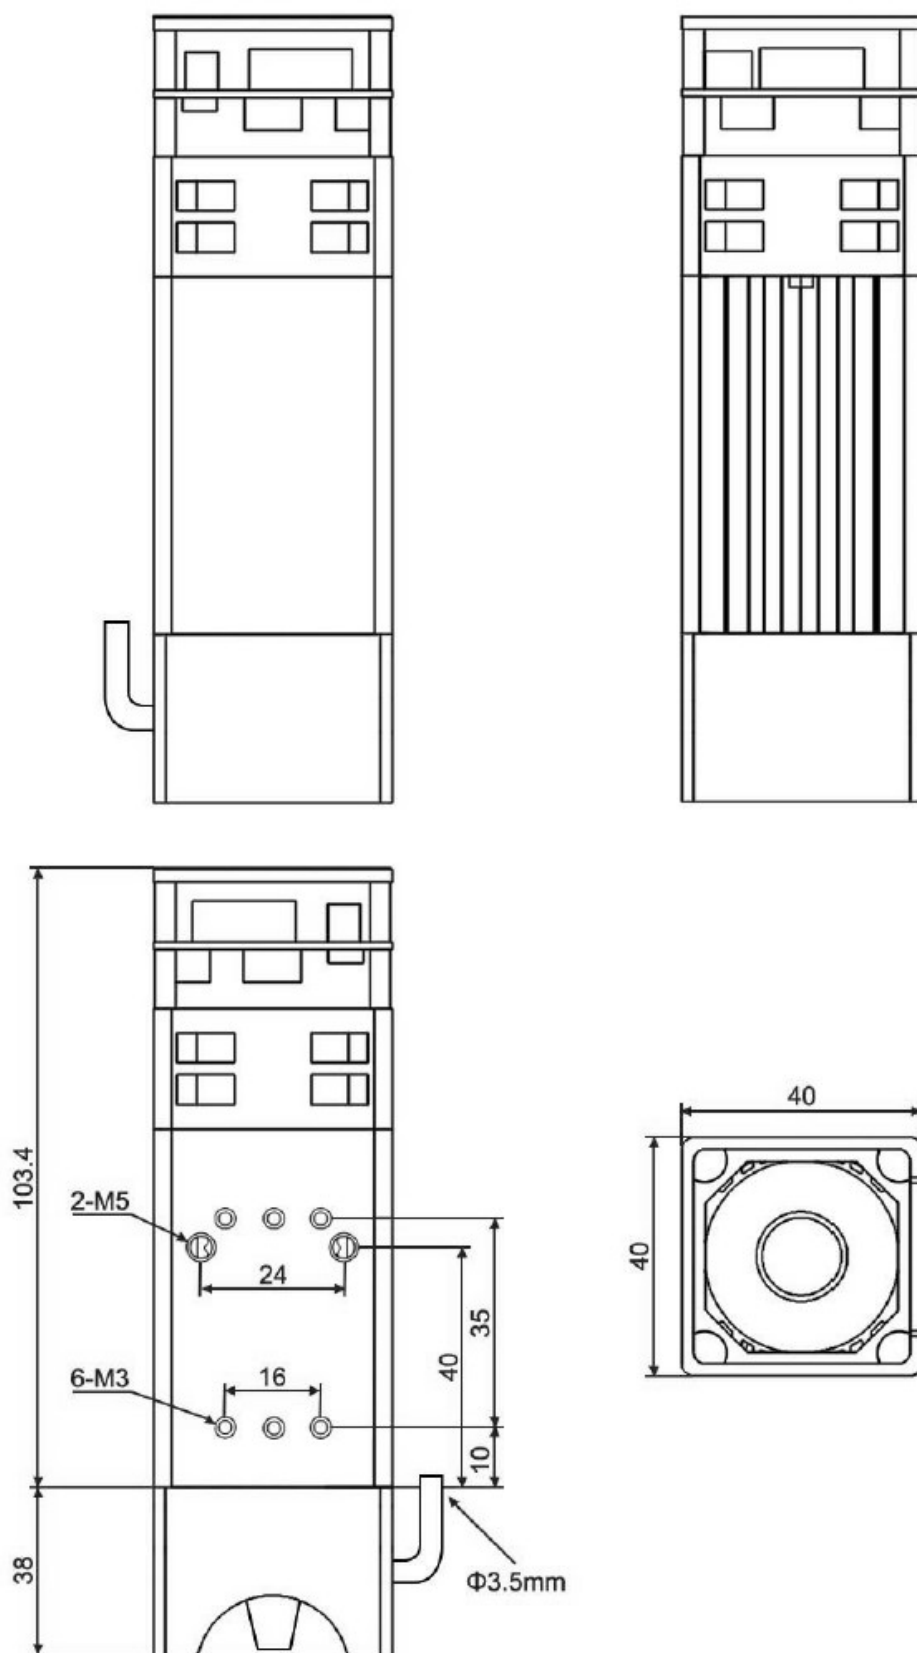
Габаритный чертеж лазерного модуля LT5W-12V.
